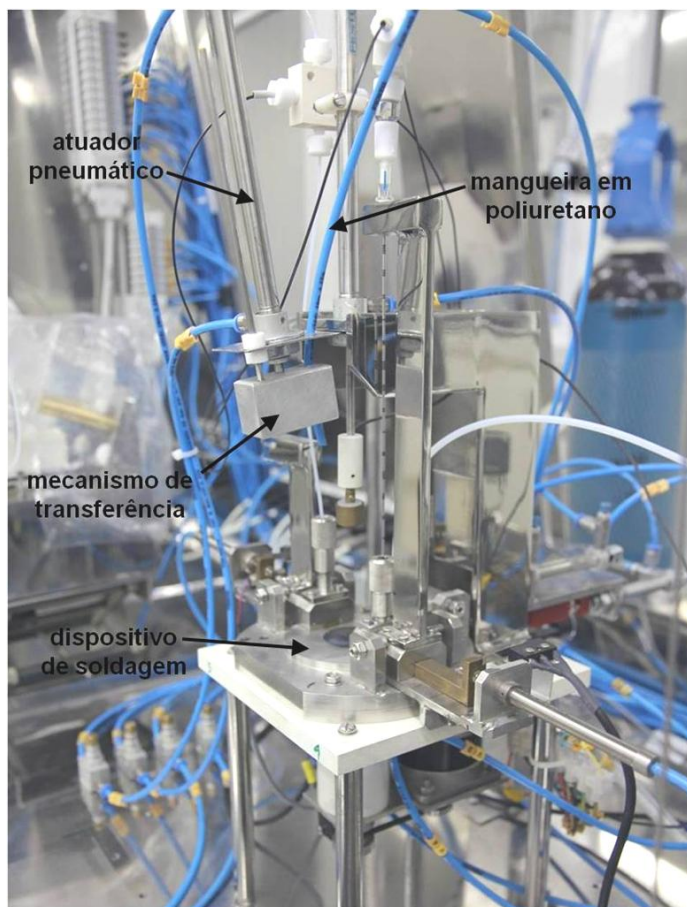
Dispositivo de soldagem a laser com mecanismo de transferência dos tubos selados rejeitados
